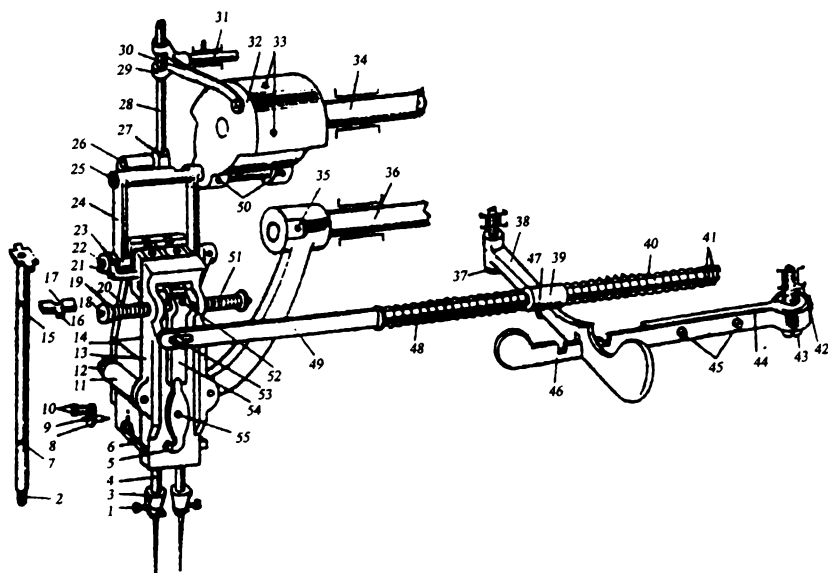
Конструкция механизма движения иглы машины 1852 кл. ПМЗ
